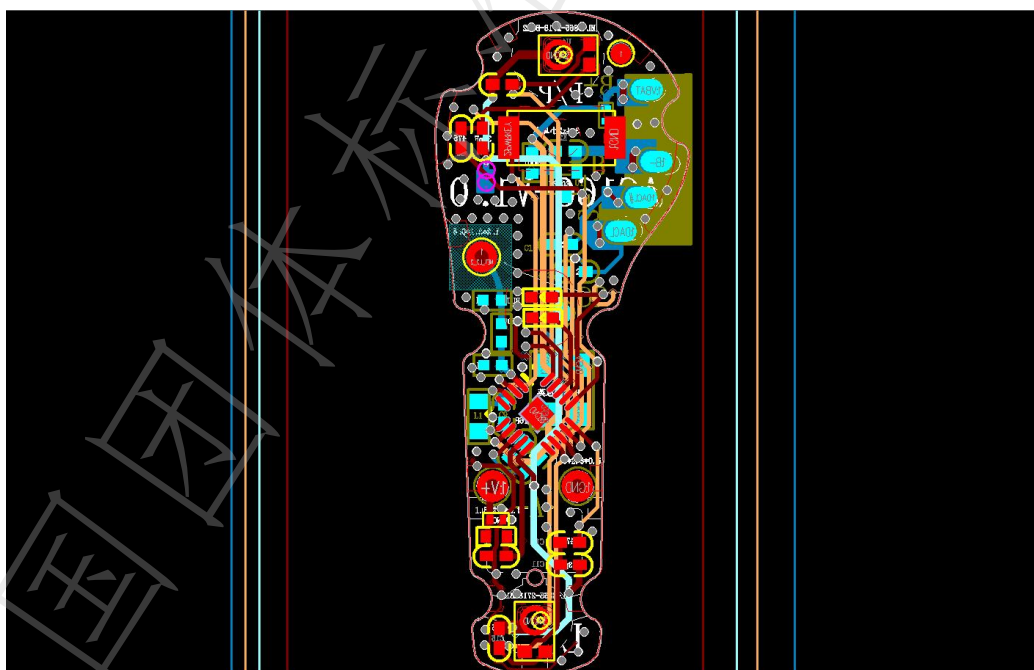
AD02-2002 (AC166) PCB 右耳设计图
